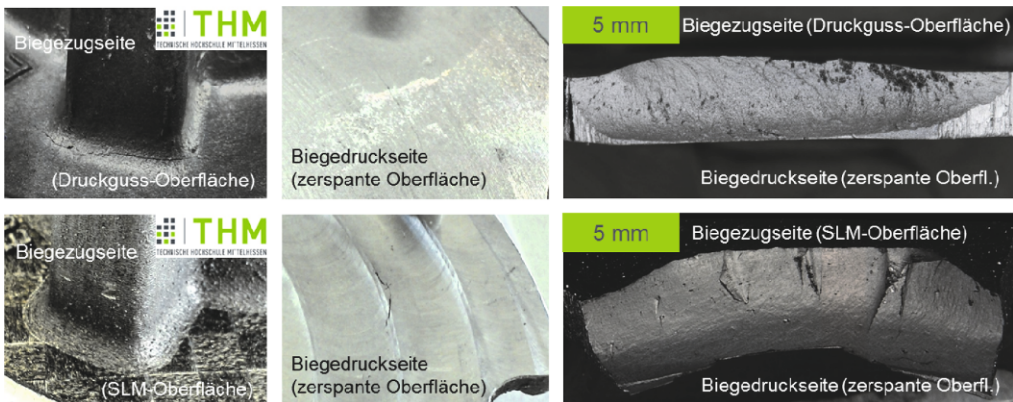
Risse und Bruchflächen von Druckguss-Bauteil (oben), SLM-Bauteil (unten)
